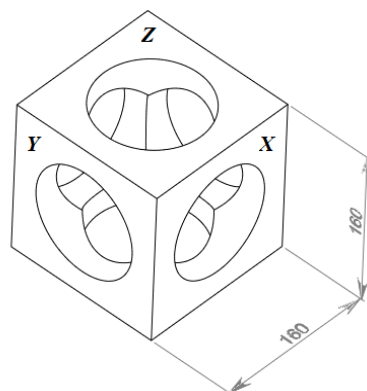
Конструкция жесткого приспособления для испытания малогабаритных изделий
